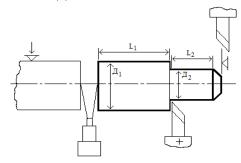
Схема обработки детали на токарно-револьверном станке
